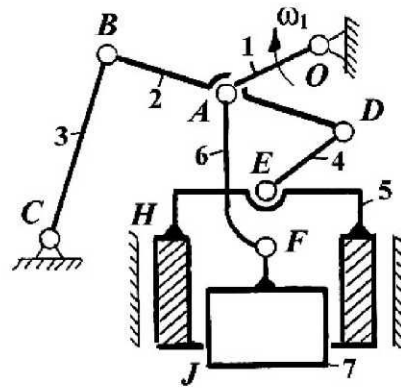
Механизм ковочно-штамповочного пресса
